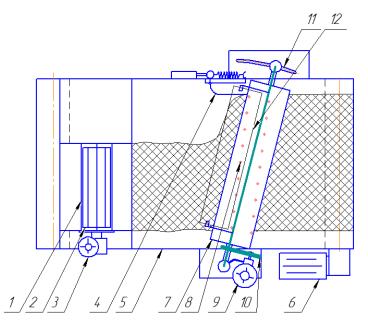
Разравнивающее устройство: 1 — бункер-дозатор, 2 — дозирующий вал, 3,6,9 — мотор-редуктор, 4 — концевая лопатка, 5 — лента конвейера, 7 — разравнивающий вал, 8 — пальцы, 10 — ременная передача, 11 — узел регулировки угла атаки, 12 — чистик.
